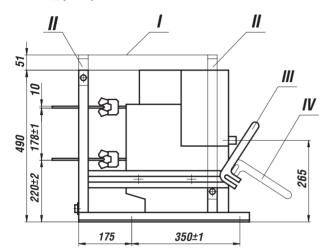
Габаритные и установочные размеры выключателей 340С в двух- и трехполюсном исполнении
